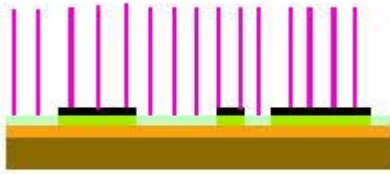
Das Layout (schwarz) wird auf die Platte gelegt. Durch Bestrahlung mit der UV-Lampe wird der Fotolack dort instabil gemacht wo das Layout ihn nicht bedeckt. (weiss-grüne Stellen)
